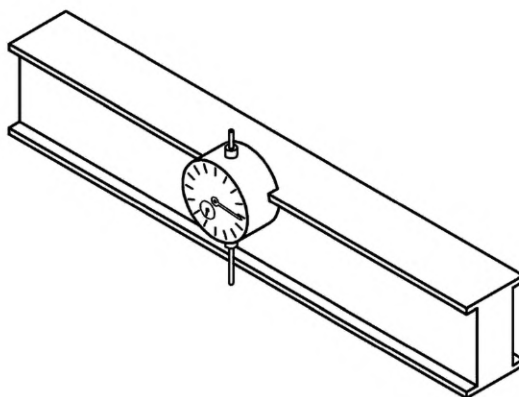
Устройство для измерения глубины роликовой волны
